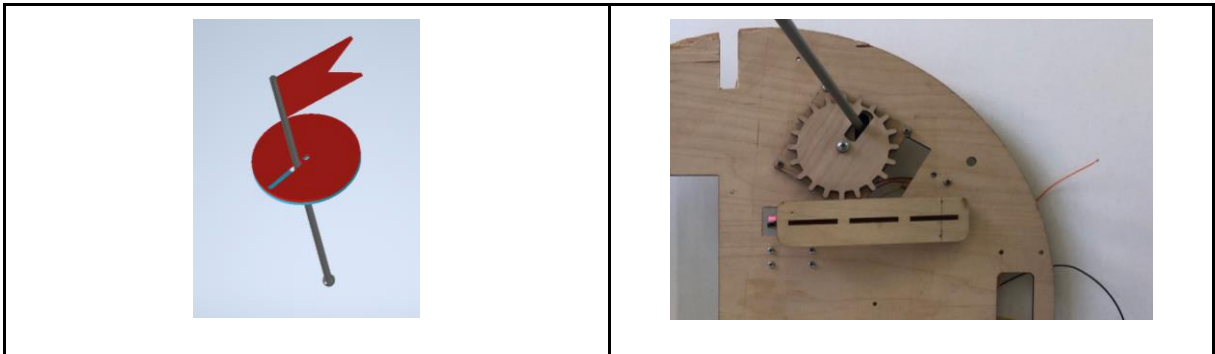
Модель движителя марионеточной опоры (сборка в Autodesk Inventor), детали изготовленного механизма
